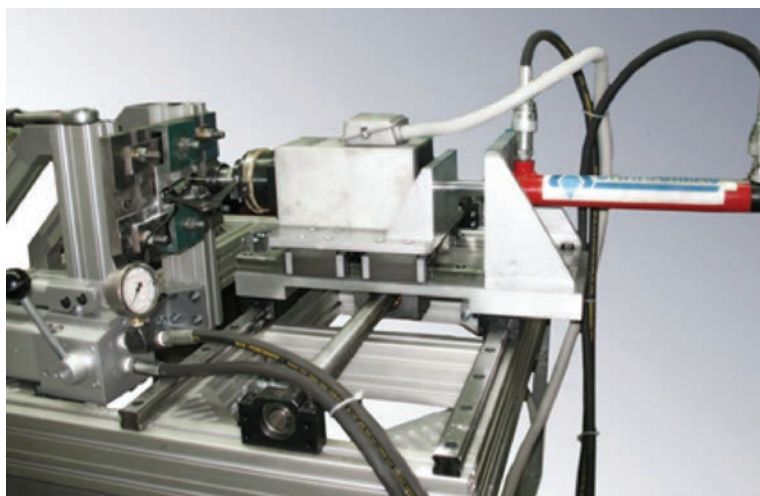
Установка для высокоскоростной сварки трением перемешиванием.
